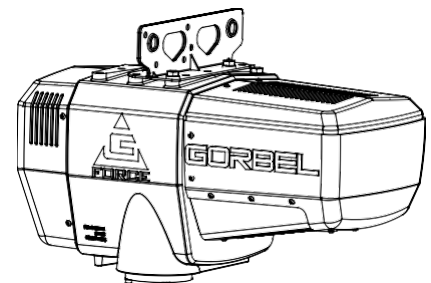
B. Standard-Antriebsbaugruppe mit Universal-Adapterwagen.
